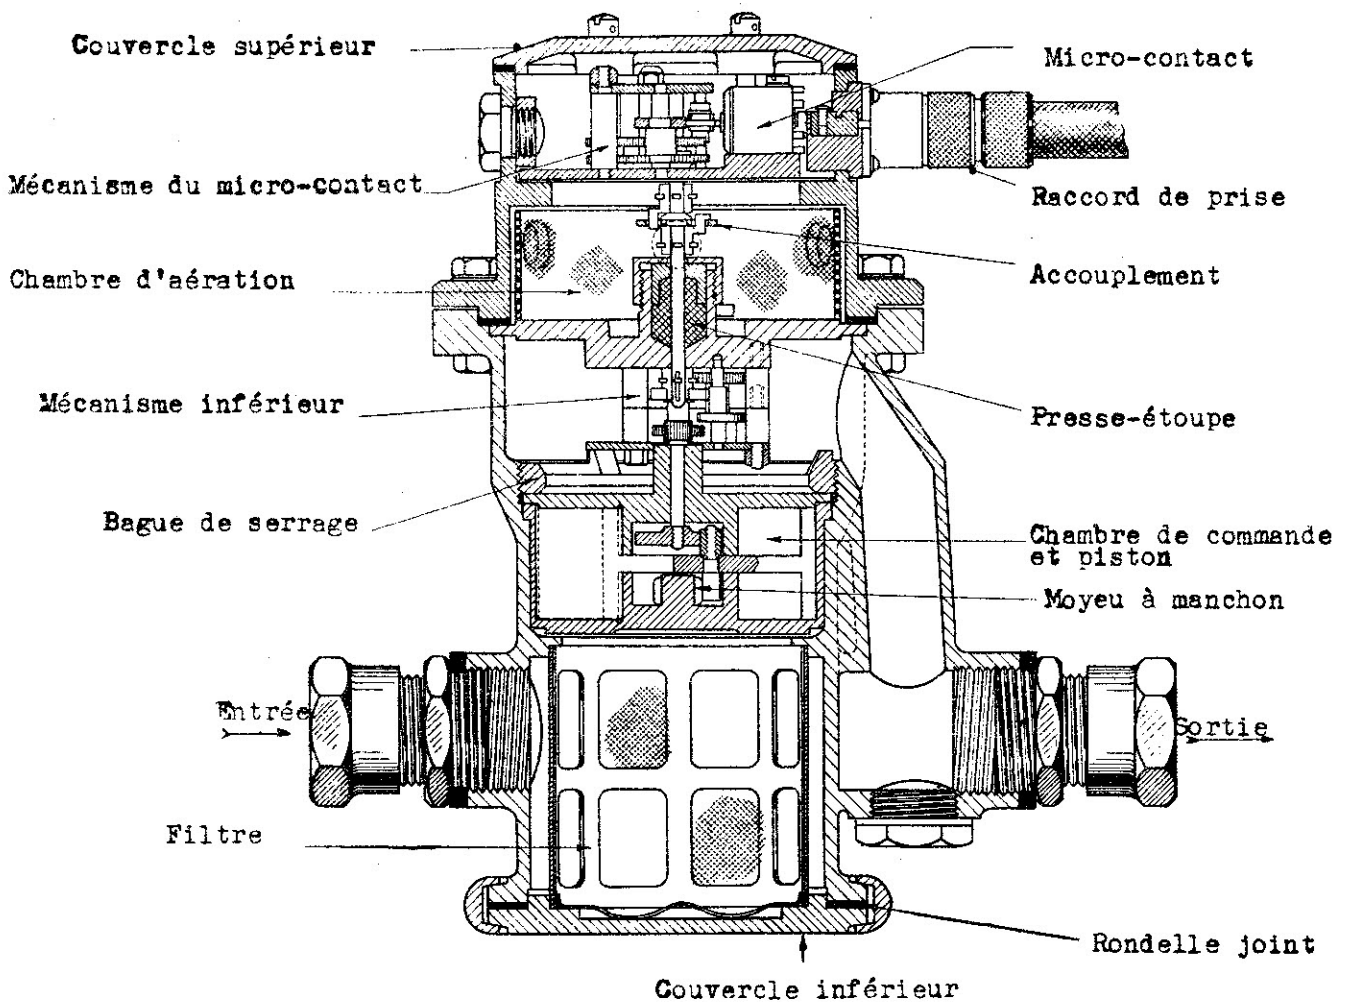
VUE EN COUPE DU TRANSMETTEUR
